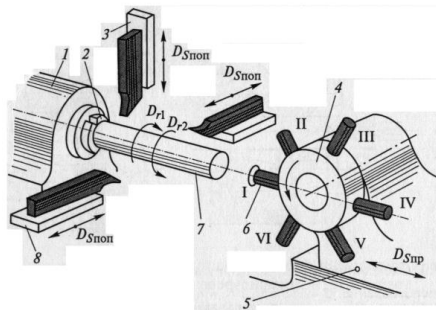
Схема обробки на токарно-револьверному автоматі:
